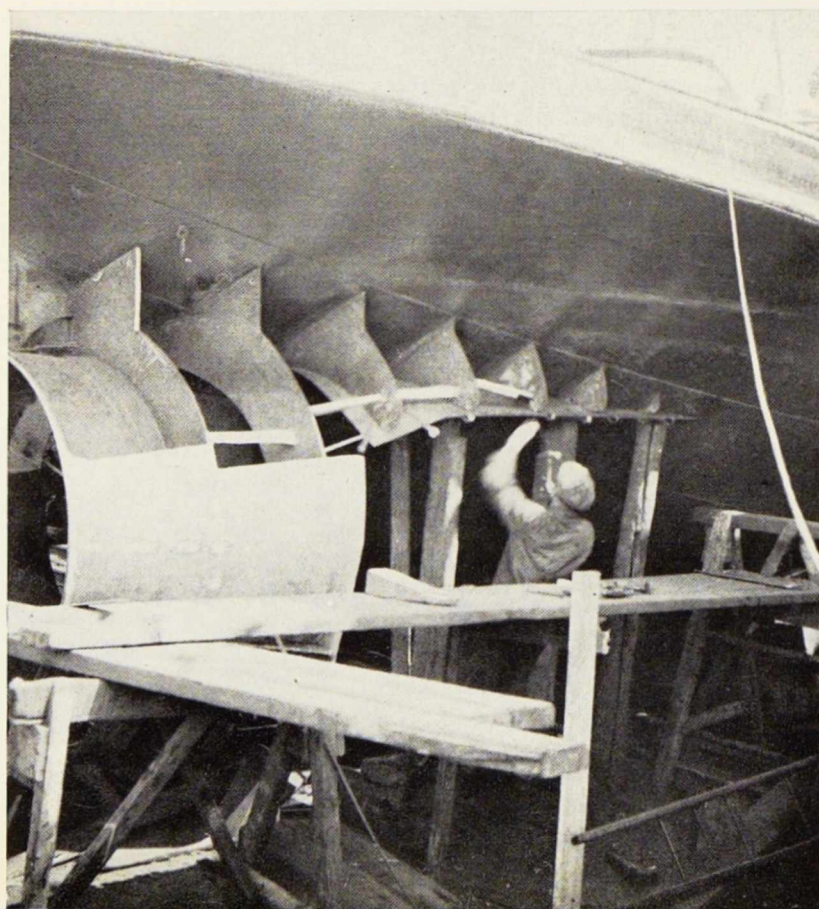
Construction soudée d'une tuyère Kort placée sur un remorqueur (chantier de Rupelmonde).
